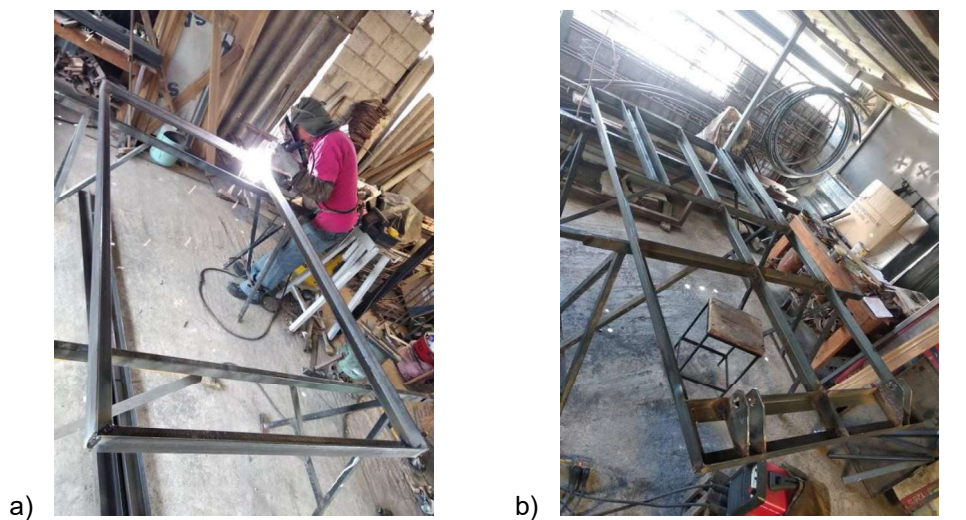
(a) Soldadura del marco del bastidor. (b) Soldadura de guías y orejas.
